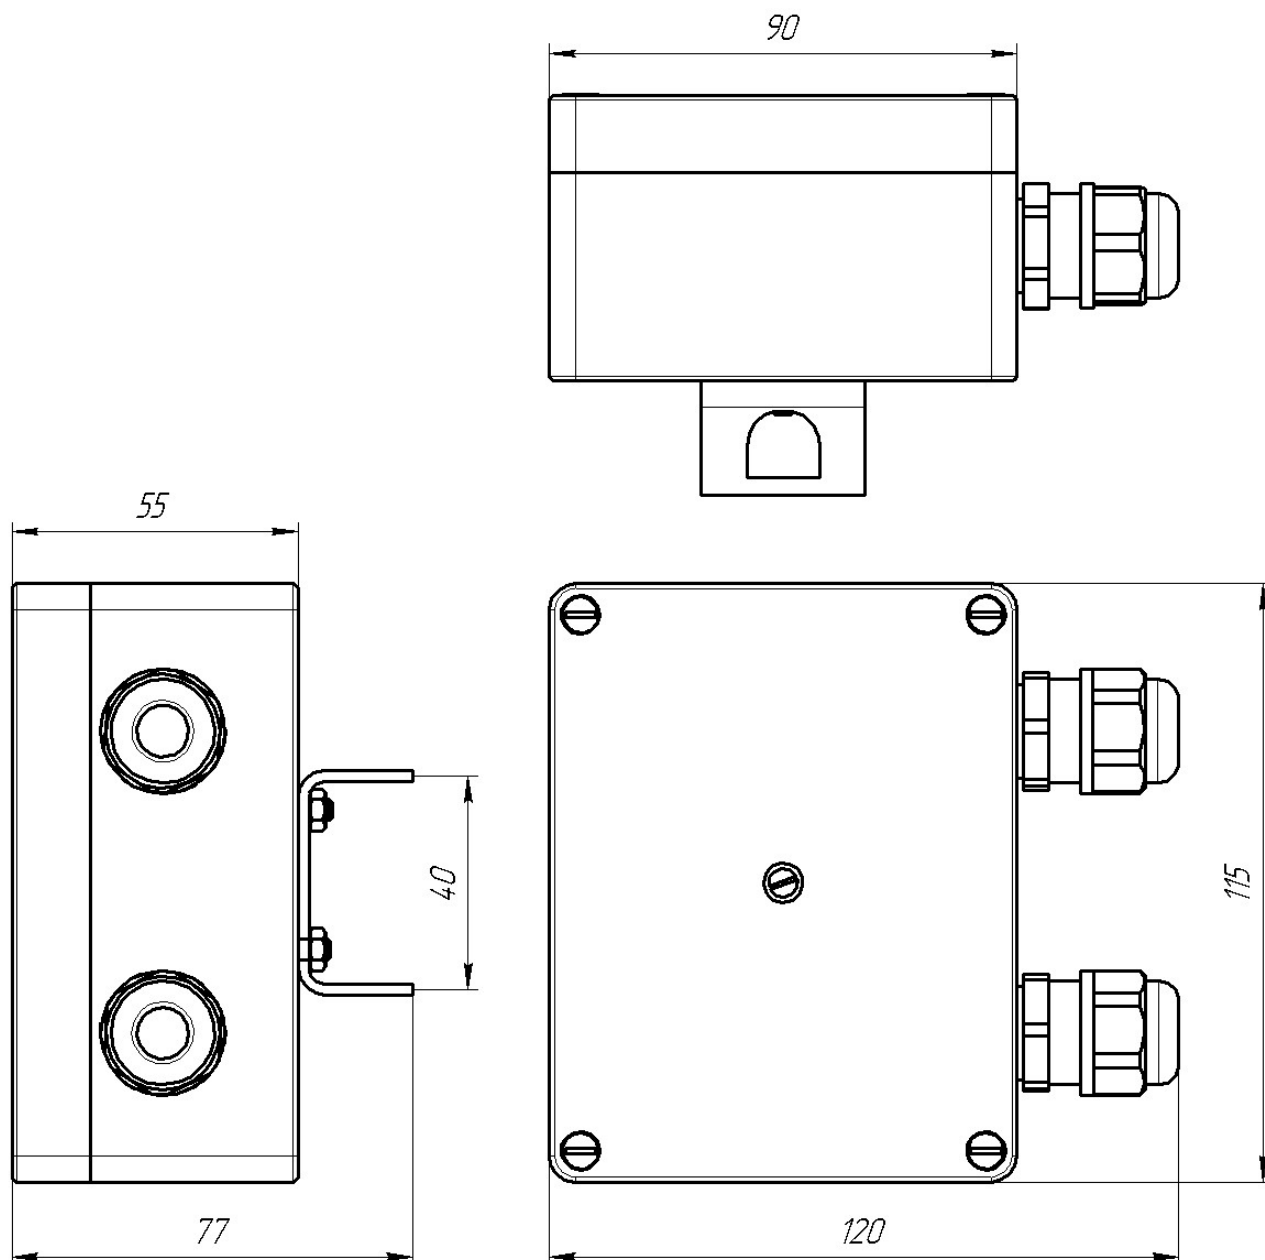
Внешний вид КР с габаритными размерами
